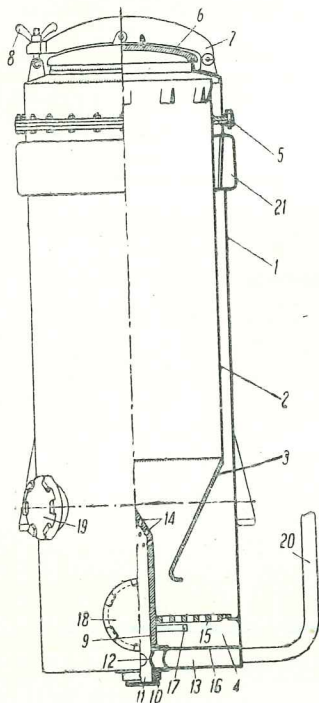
Схема газогенератора установки ЛТА для автомобиля ЗИС-5
